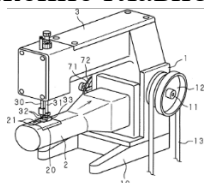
Общий вид промышленной универсальной швейной машины цепного стежка с рукавной платформой, представленной в патенте JP4228368B2 (стрелка показывает направление движения ткани)
